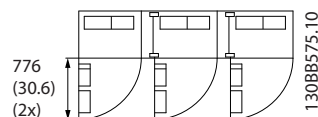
Пространство перед корпусом типа IP21/IP54, типоразмер F11
